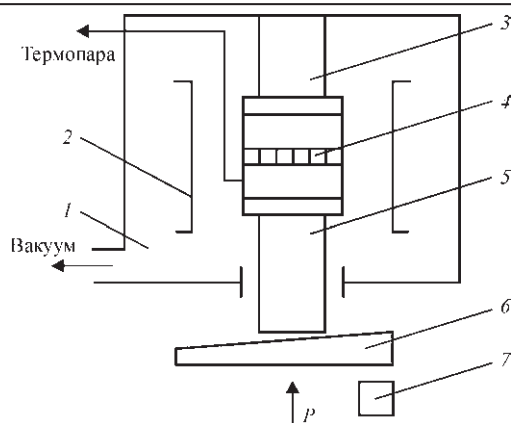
Схема рабочей камеры с оснасткой: 1 — рабочая камера; 2 — нагреватель из молибдена; 3 — верхний шток; 4 — трехслойная панель, установленная в ограничивающую втулку; 5 — нижний шток; 6 — клин; 7 — пресс
